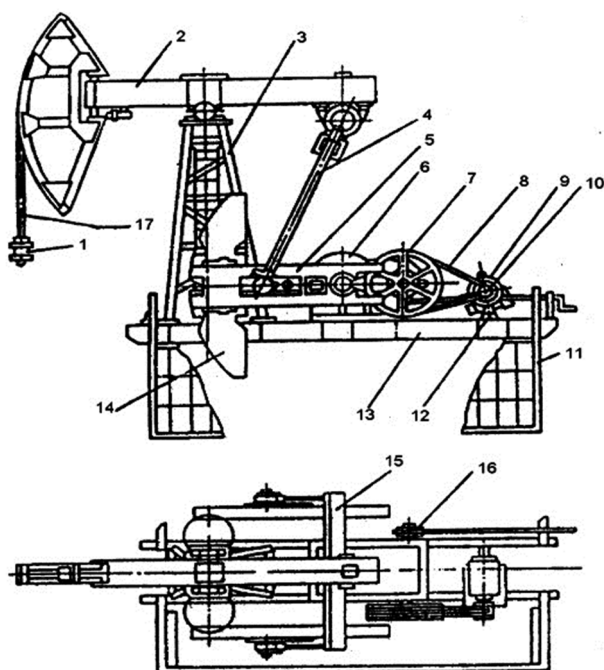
Станок-качалка типа СКД: 1 – подвеска устьевых штока; 2 – балансир с опорой; 3 – стойка; 4 – шатун; 5 – кривошип; 6 – редуктор; 7 – ведомый шкив; 8 – ремень; 9 – электродвигатель; 10 – ведущий шкив; 11 – ограждение; 12 – поворотная плита; 13 – рама; 14 – противовес; 15 – траверса; 16 – тормоз; 17 – канатная подвеска
